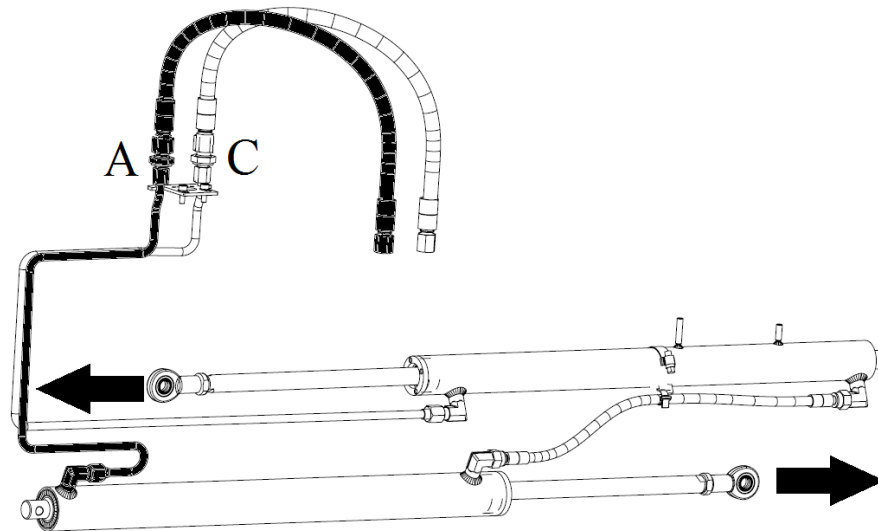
Hydraulische Anlage für die Ausführungen ohne Seitenschub und mit Standardposition der Zinkenversorgungsingängen
